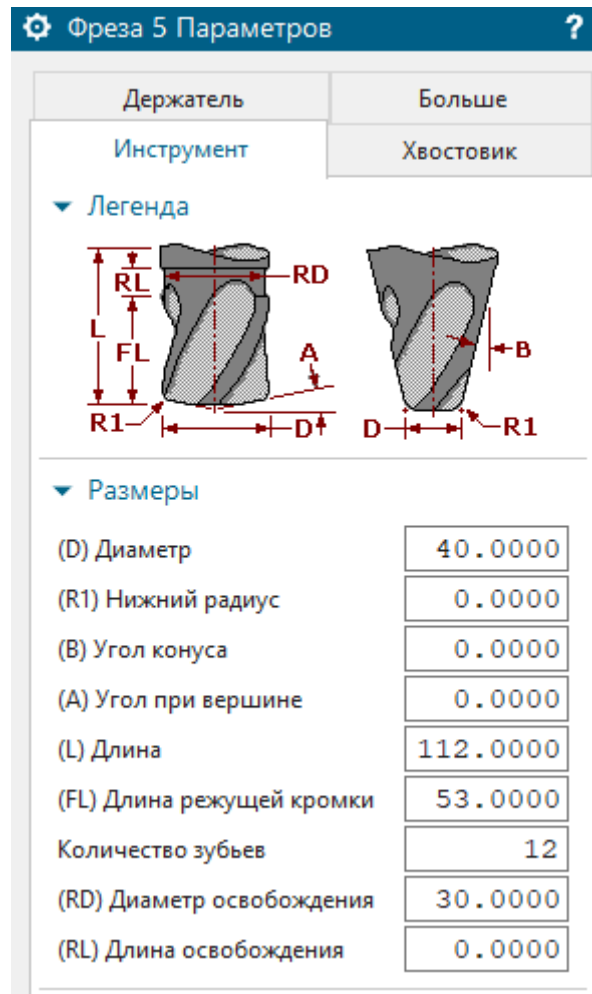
Створення ріжучого інструменту – фреза
